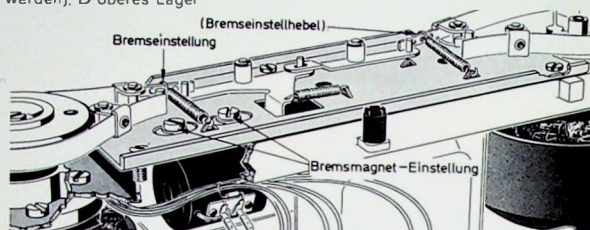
Blick auf und unter das Bremschassis; durch Umhängen der Feder am Brems einstellenhebel wird der Federzug verändert
